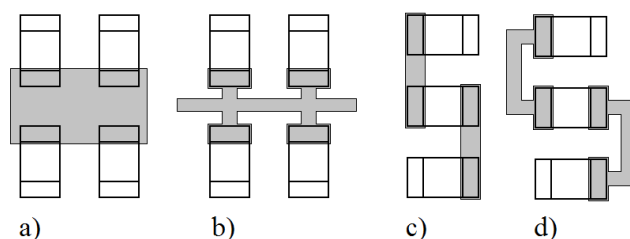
Vhodný směr pro pájení vlnou [4]
